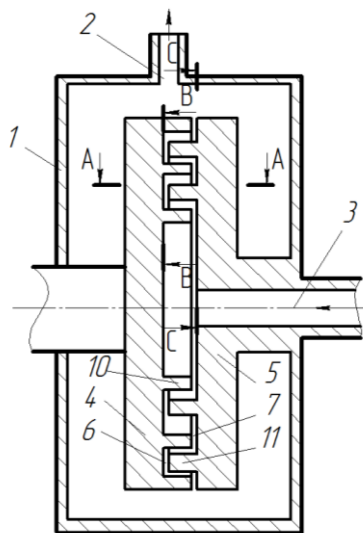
Схема загального вигляду гідродинамічного кавітаційного реактора: 1 – корпус; 2 – вхідний отвір; 3 – вхідний отвір; 4 – ротор; 5 – статор; 6 – пази ротора; 7 – пази статора; 10,11 – виступи
